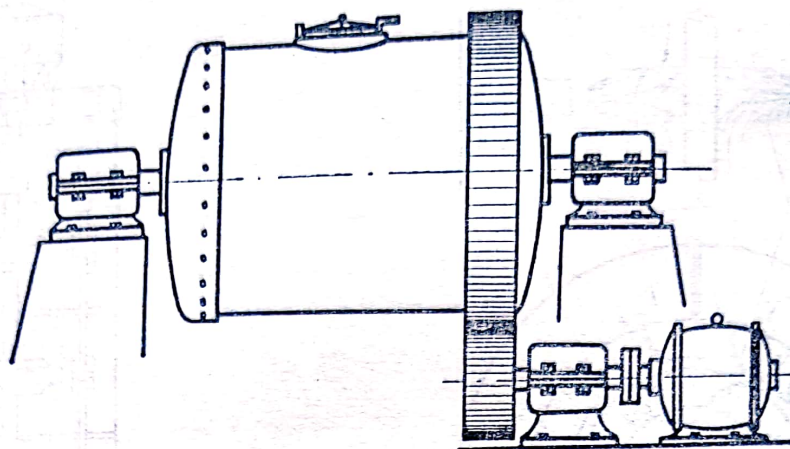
Amestecătorul cu tambur cilindric orizontal.
